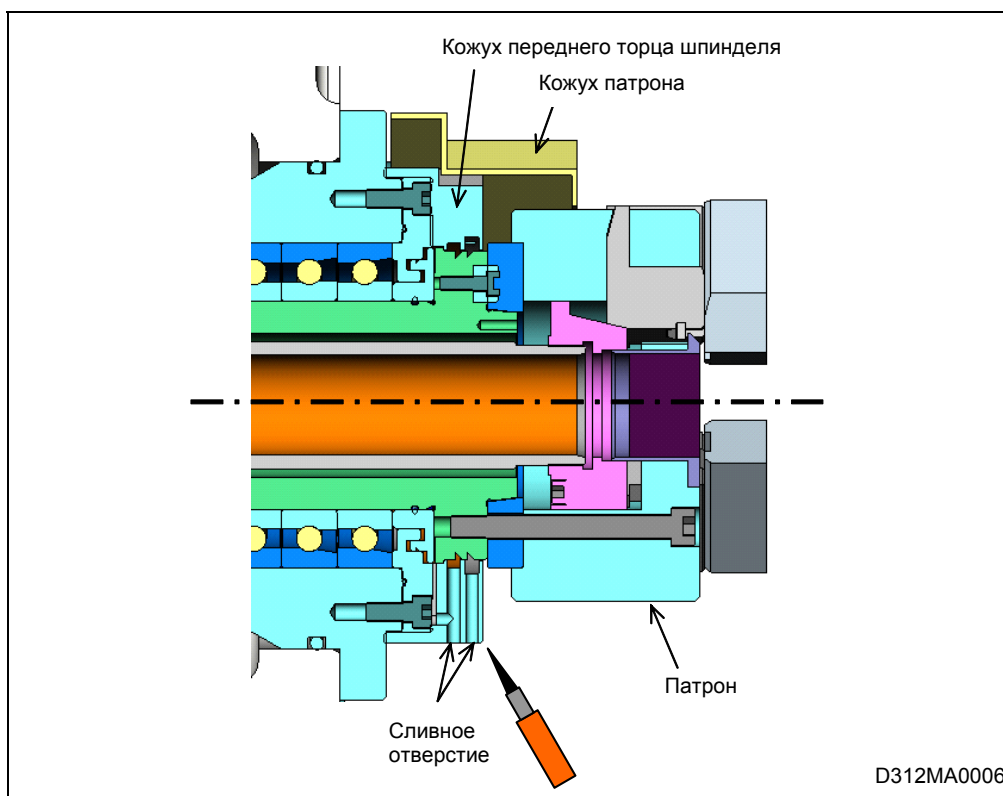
Чистка сливных отверстий под кожухом переднего торца шпинделя
